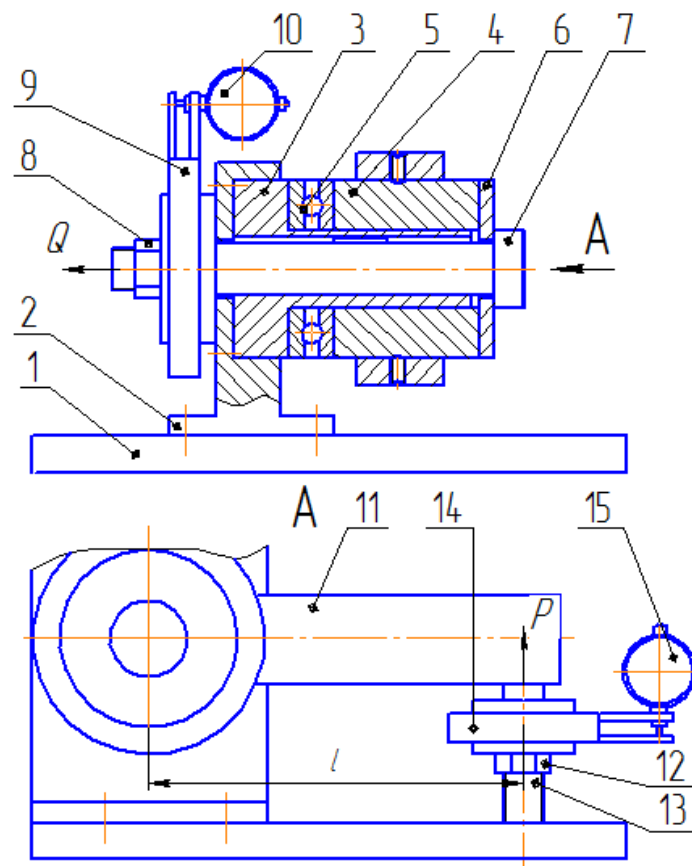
Конструктивная схема установки для определения сил закрепления заготовок на оправках с зазором и упором в торец
